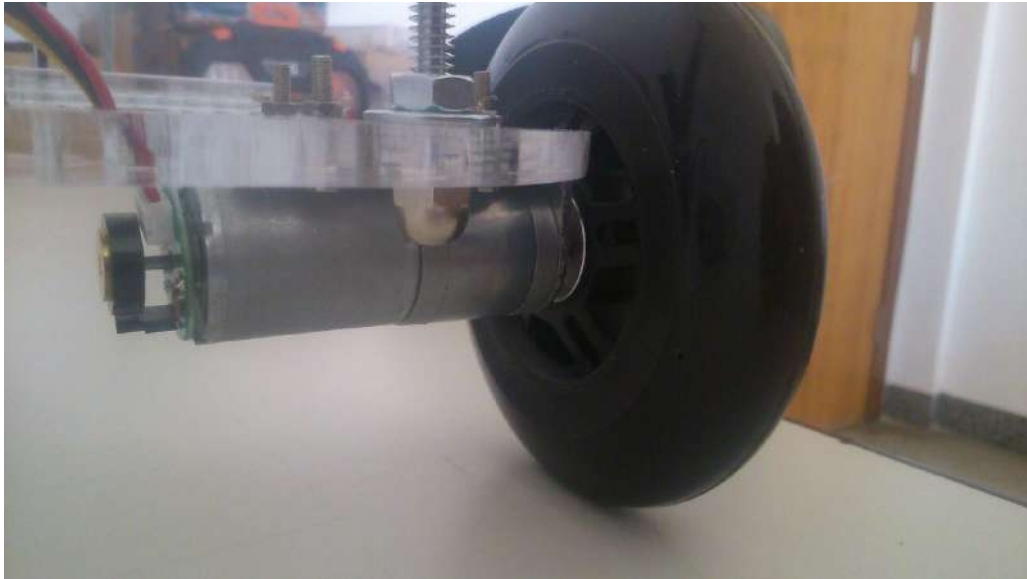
Montagem final do mecanismo de acoplamento do motor à roda.
